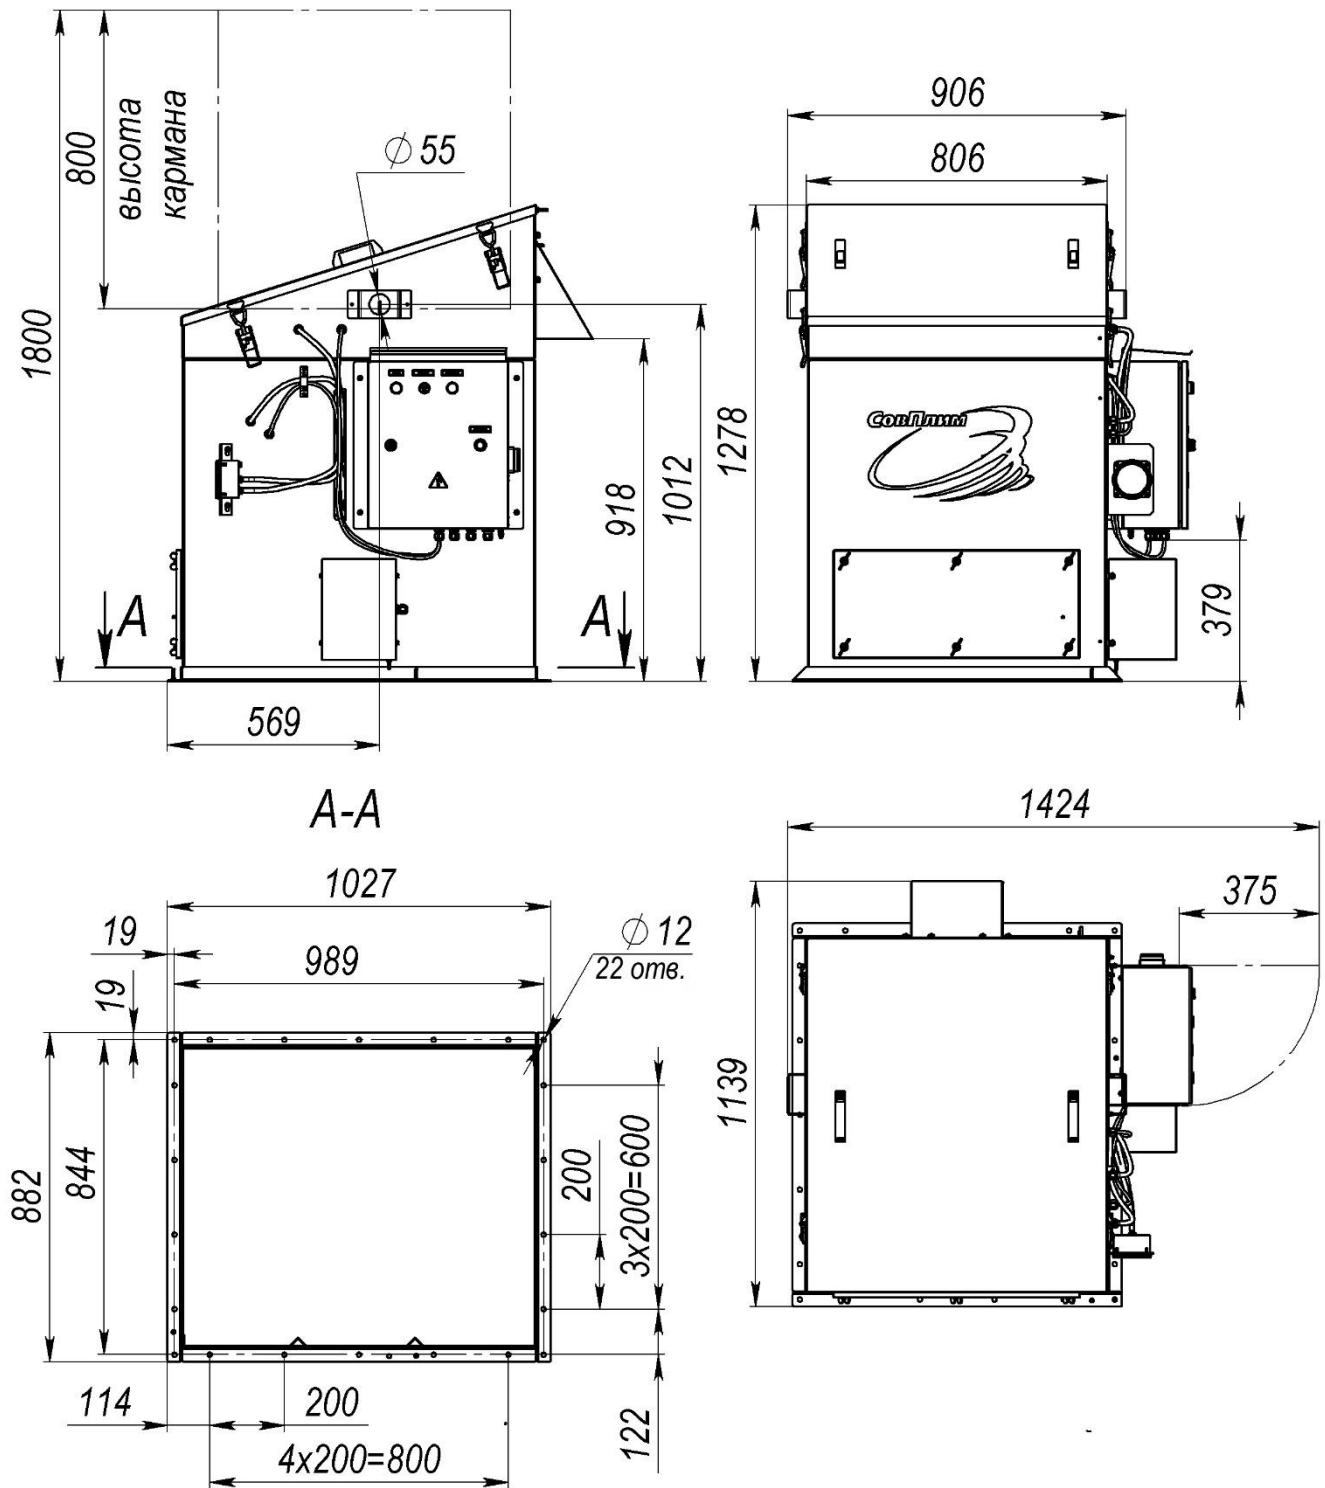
Габаритные размеры фильтра напорного типа (модели SFM-20)
